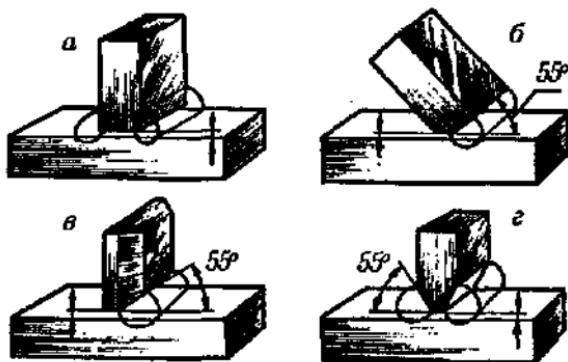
Тавровые соединения сваркой: а — под прямым углом без скоса кромок; б — под углом со скосом одной кромки; в — под прямым углом со скосом одной кромки; г — под прямым углом с двусторонним скосом кромок.
